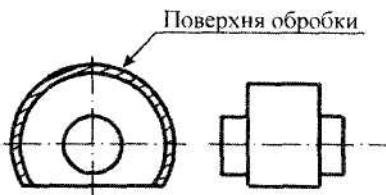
Схема формоутворення круглої циліндричної поверхні торцевою фрезою із зубом, що зачищає
